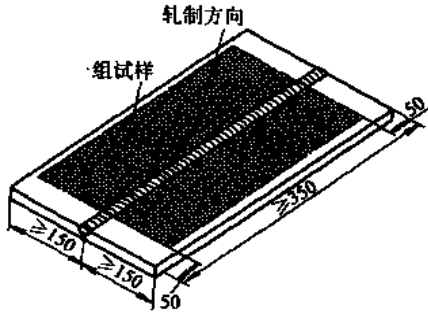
焊条电弧焊和半机械化焊接对接接头试件
